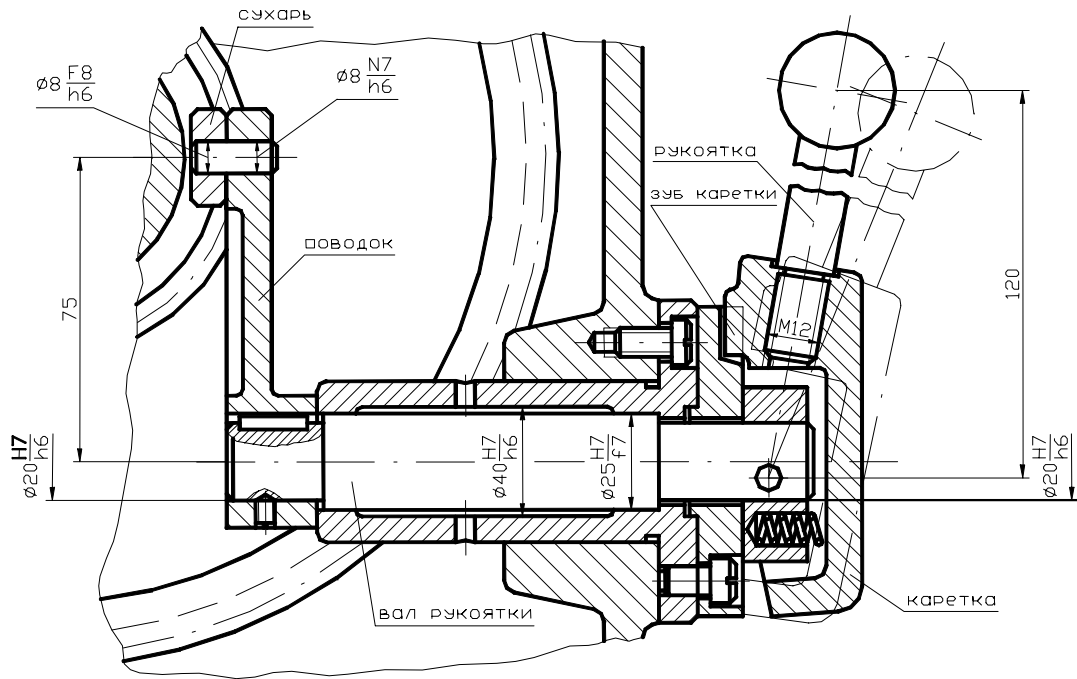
Рычажный механизм управления муфтой с односторонним рычагом, смонтированный на одной стенке корпуса
